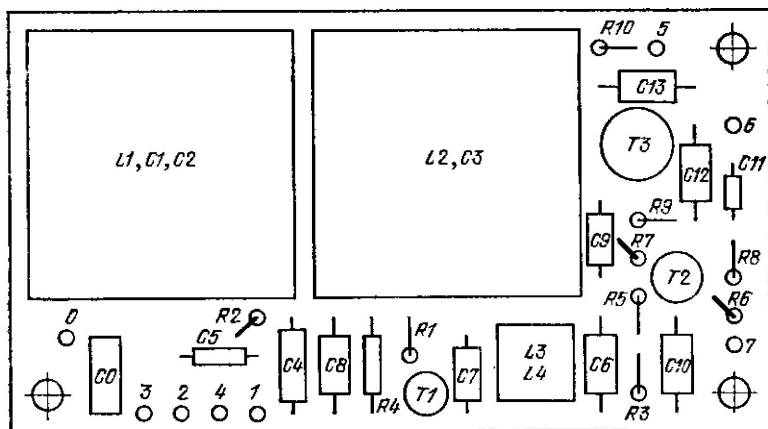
Монтажная схема платы второго смесителя (вид сверху)
